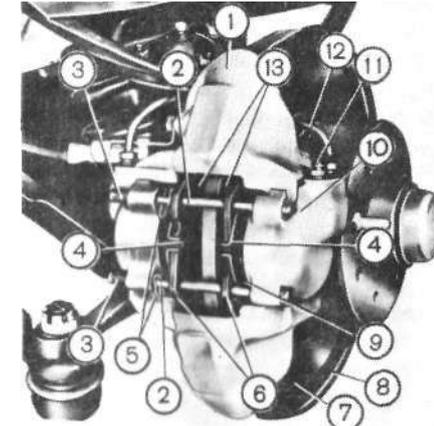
Передний дисковый тормоз: 1 — суппорт; 2 — пальцы крепления тормозных колодок; 3 — пружины; 4 — пружины; 5 — шпильки; 6 — тормозные колодки; 7 — тормозной диск; 8 — кожух диска; 9 — поршень тормозного цилиндра; 10 — тормозной цилиндр; 11 — штуцер; 12 — соединительная трубка; 13 — фрикционные накладки
